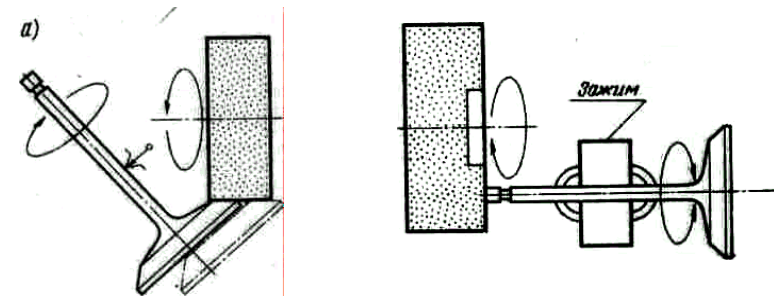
Схема шлифования фаски (а) и торца (б) клапана
